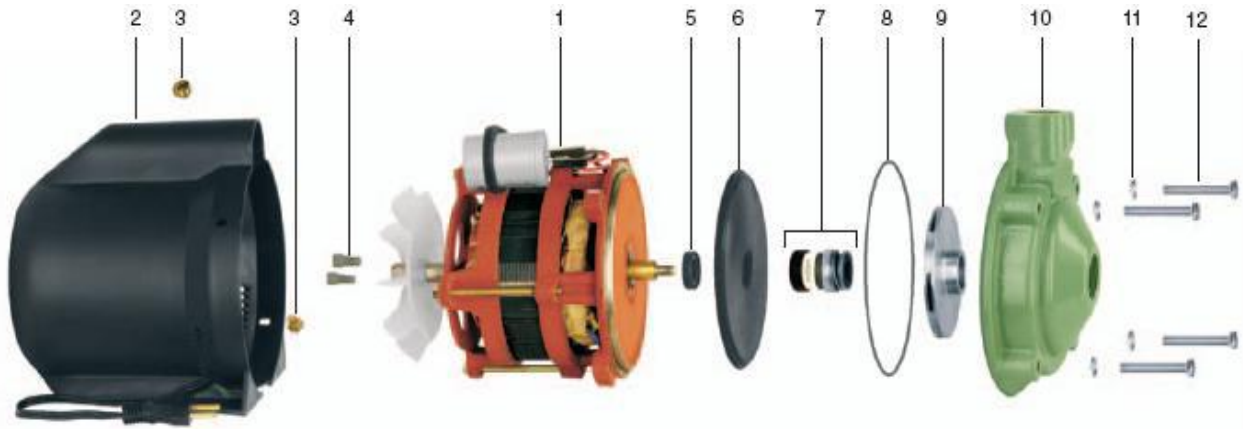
Componentes da bomba em estudo: motor elétrico 2 pólos, 2- capa com cabo de ligação, 3- parafusos PCPZ M4 x 6, 4- conector, 5- retentor, 6- junta de proteção, 7- selo mecânico, 8- o-ring, 9- rotor, 10- carcaça, 11- arruela de pressão, 12- parafusos ¼ x 2” Fonte: SCHNEIDER, 2009.
